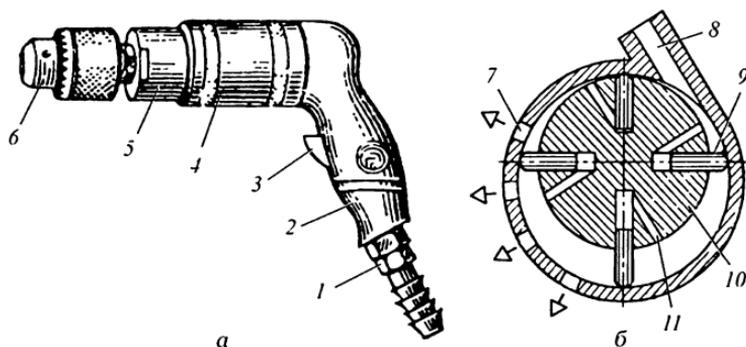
Ручная пневматическая машина: а — общий вид; б — разрез; 1 — шуцер; 2 — рукоятка; 3 — курок; 4 — корпус пневматического двигателя; 5 — корпус шпинделя; 6 — патрон; 7 — отверстие; 8 — впускное отверстие; 9 — лопатка; 10 — ротор; 11 — уравновешивающее отверстие
